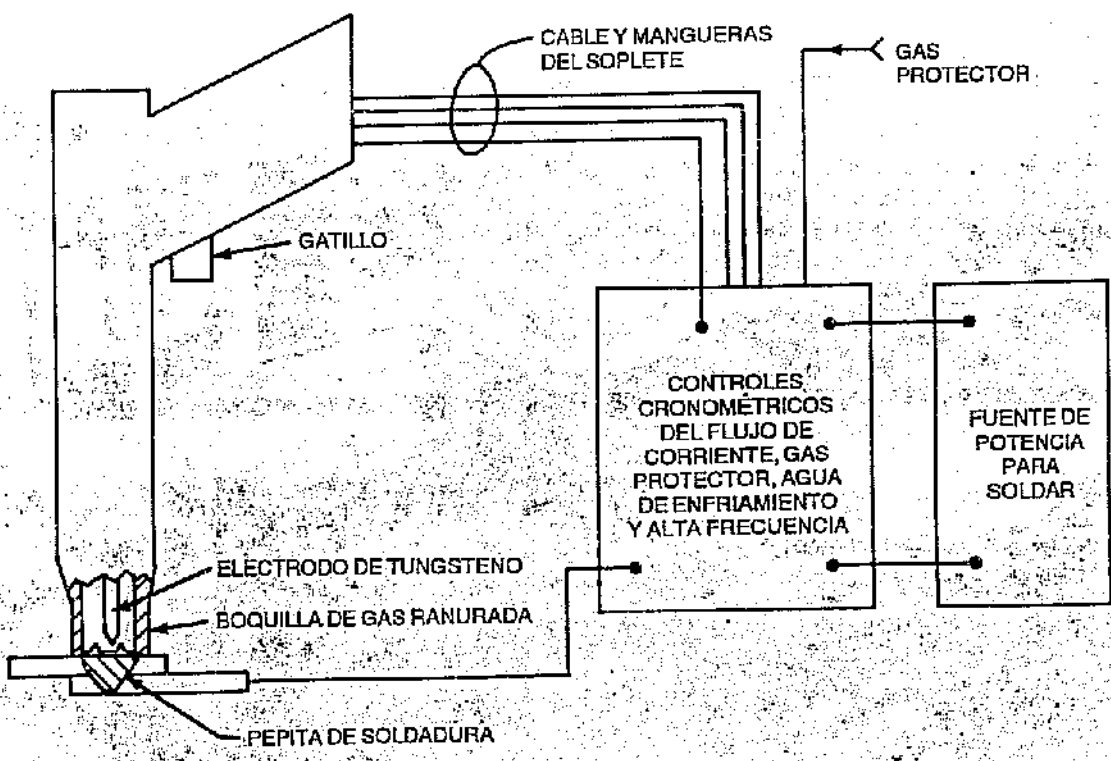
Esquema de la soldadura de puntos manual por arco de tungsteno y gas
